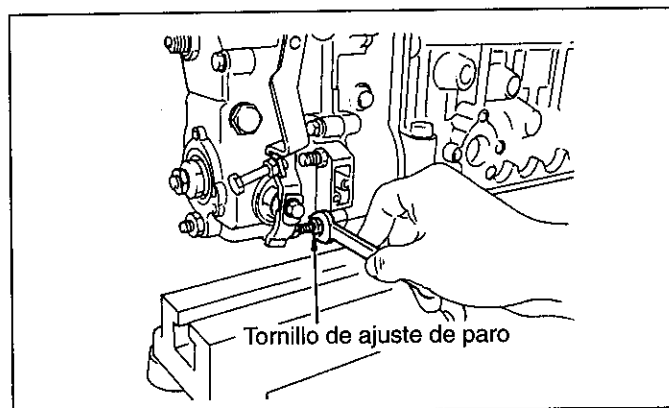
Ajuste del tornillo de ajuste de paro
